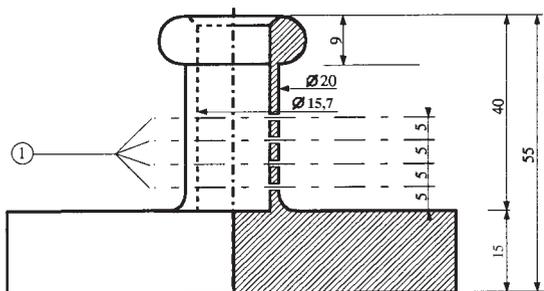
Полый бронзовый цилиндр, закрытый с одной стороны; чертеж и размеры детали в мм
